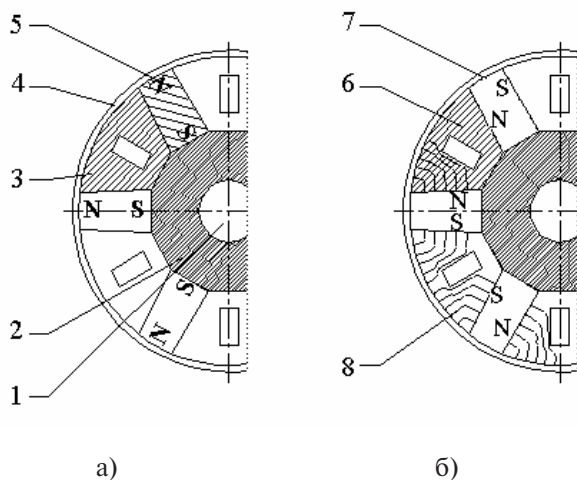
Ротор вентильного двигателя с клиновидными диаметральными (а) и тангенциальными (б) магнитами
